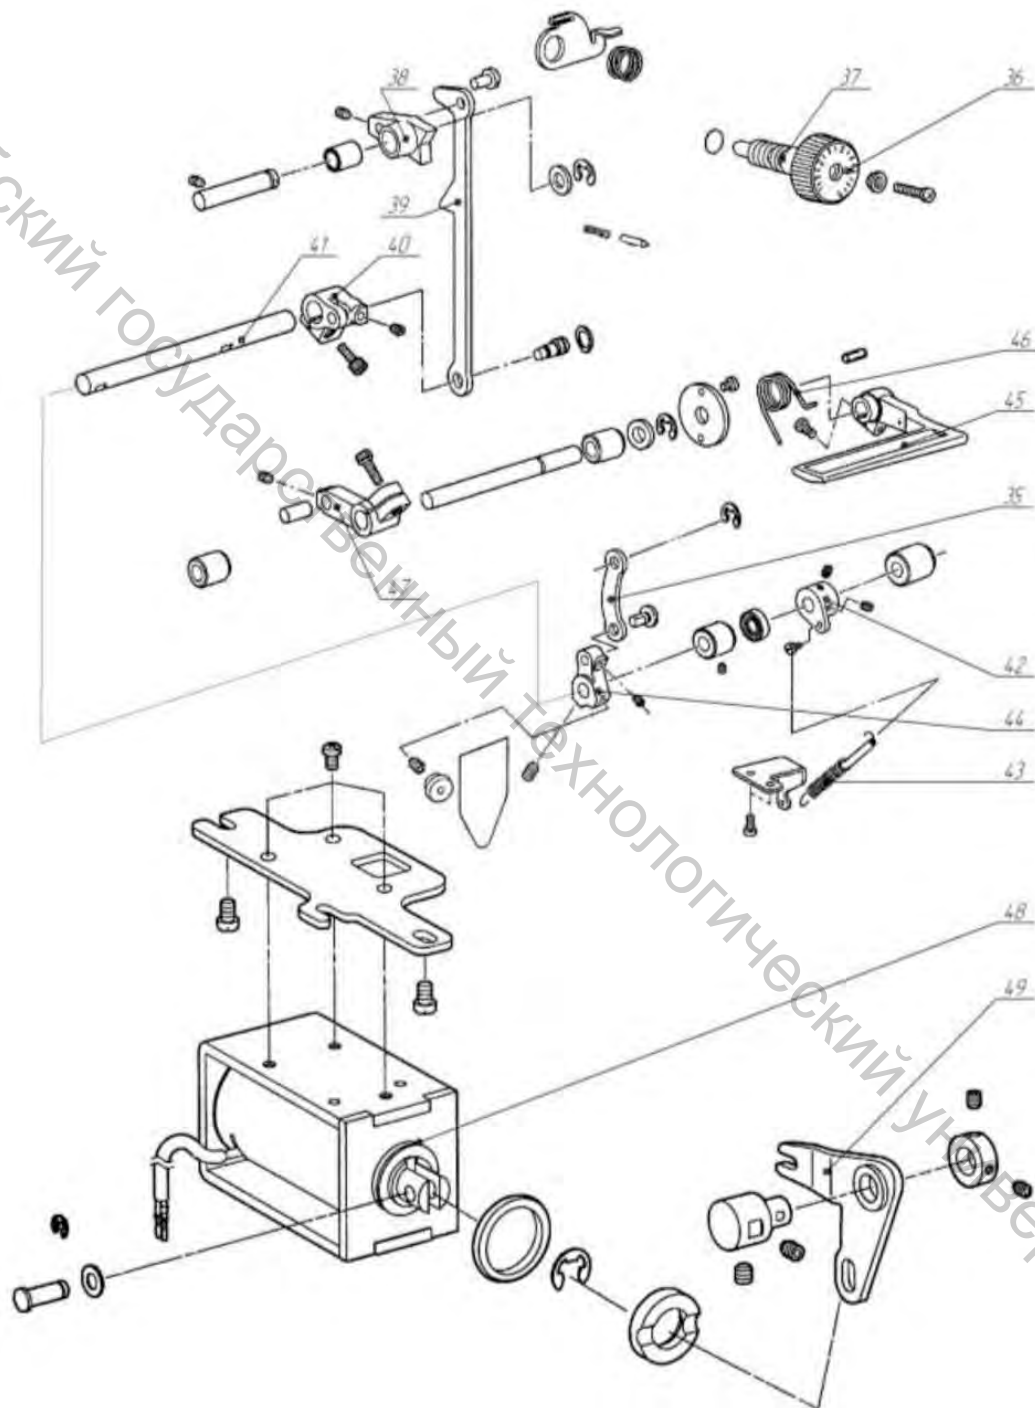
Узел регулировки длины стежка и закрепления строчки
